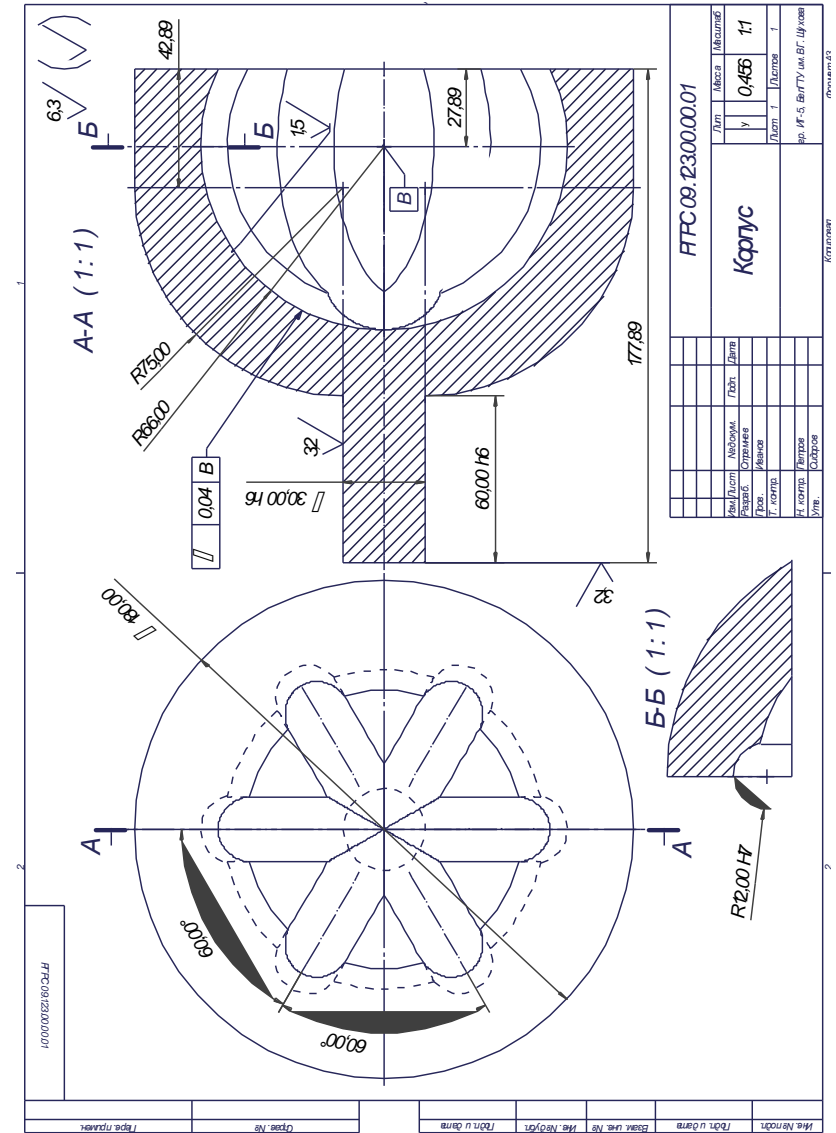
Чертеж детали “Корпус” сферического шарнира
